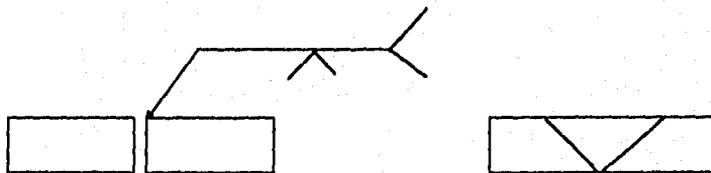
Efectuar la soldadura en placas colocadas a tope, con preparación en "V", en la parte superior.
